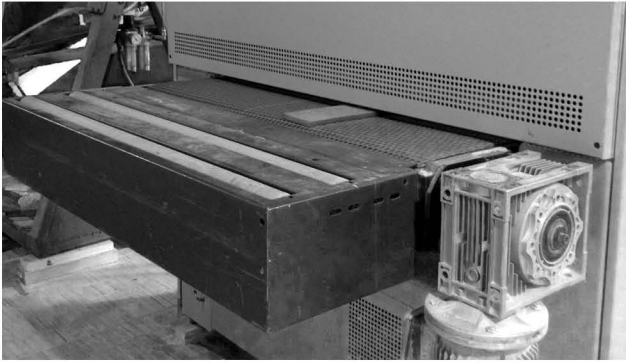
Corte y lijado. Fotografía propia, 2015.
